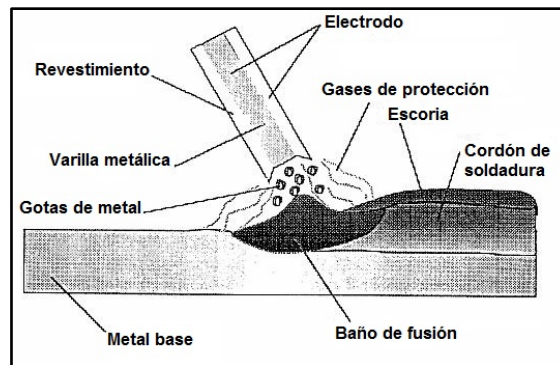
Soldadura por arco manual con electrodo revestido para acero inoxidable [12]
